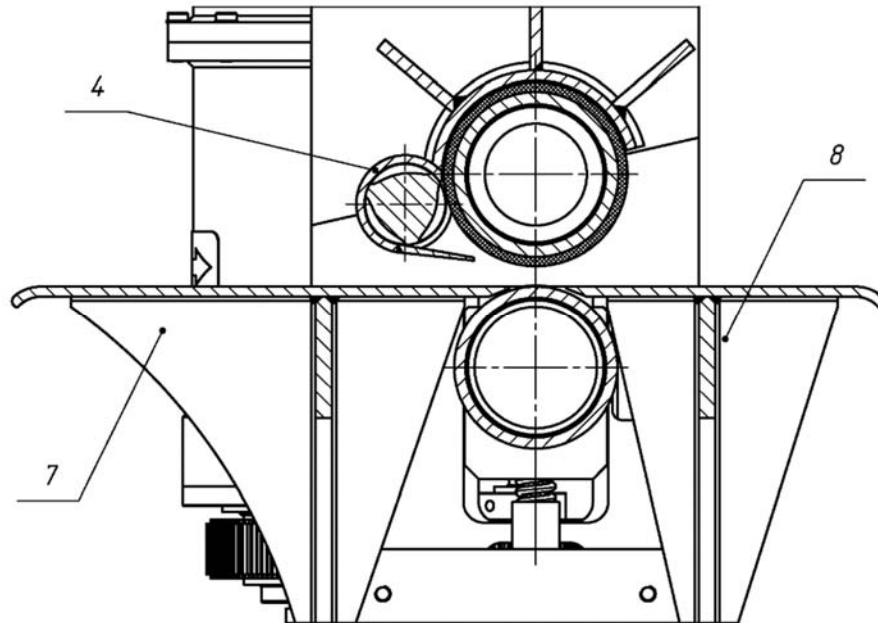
Розріз формувача перпендикулярно осі валка нагнітання
